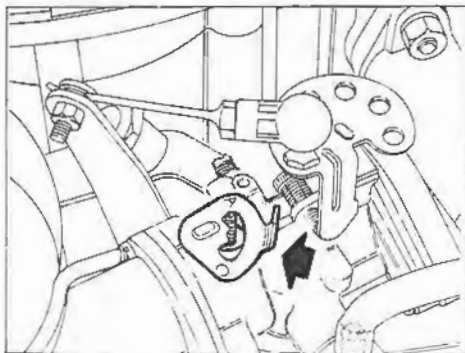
Portare la leva sulla posizione "C" a motore avviato spostarla sulla posizione "A". Hebel auf Position "C" rücken. Sobald der Motor angesprungen ist, auf "A" zurückstellen. Poner la palanca en la posición "C". Cuando el motor haya arrancado poner en la posición "A".
